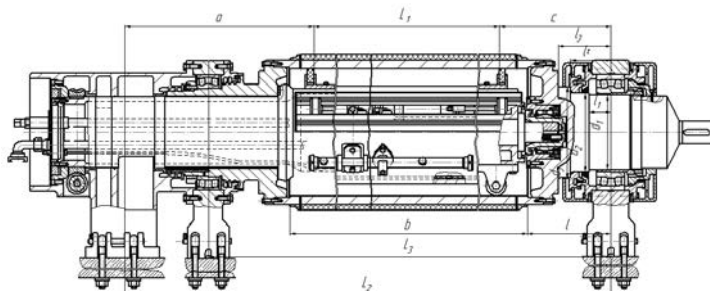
Вакум-пересасывающий вал трехвального пресса
